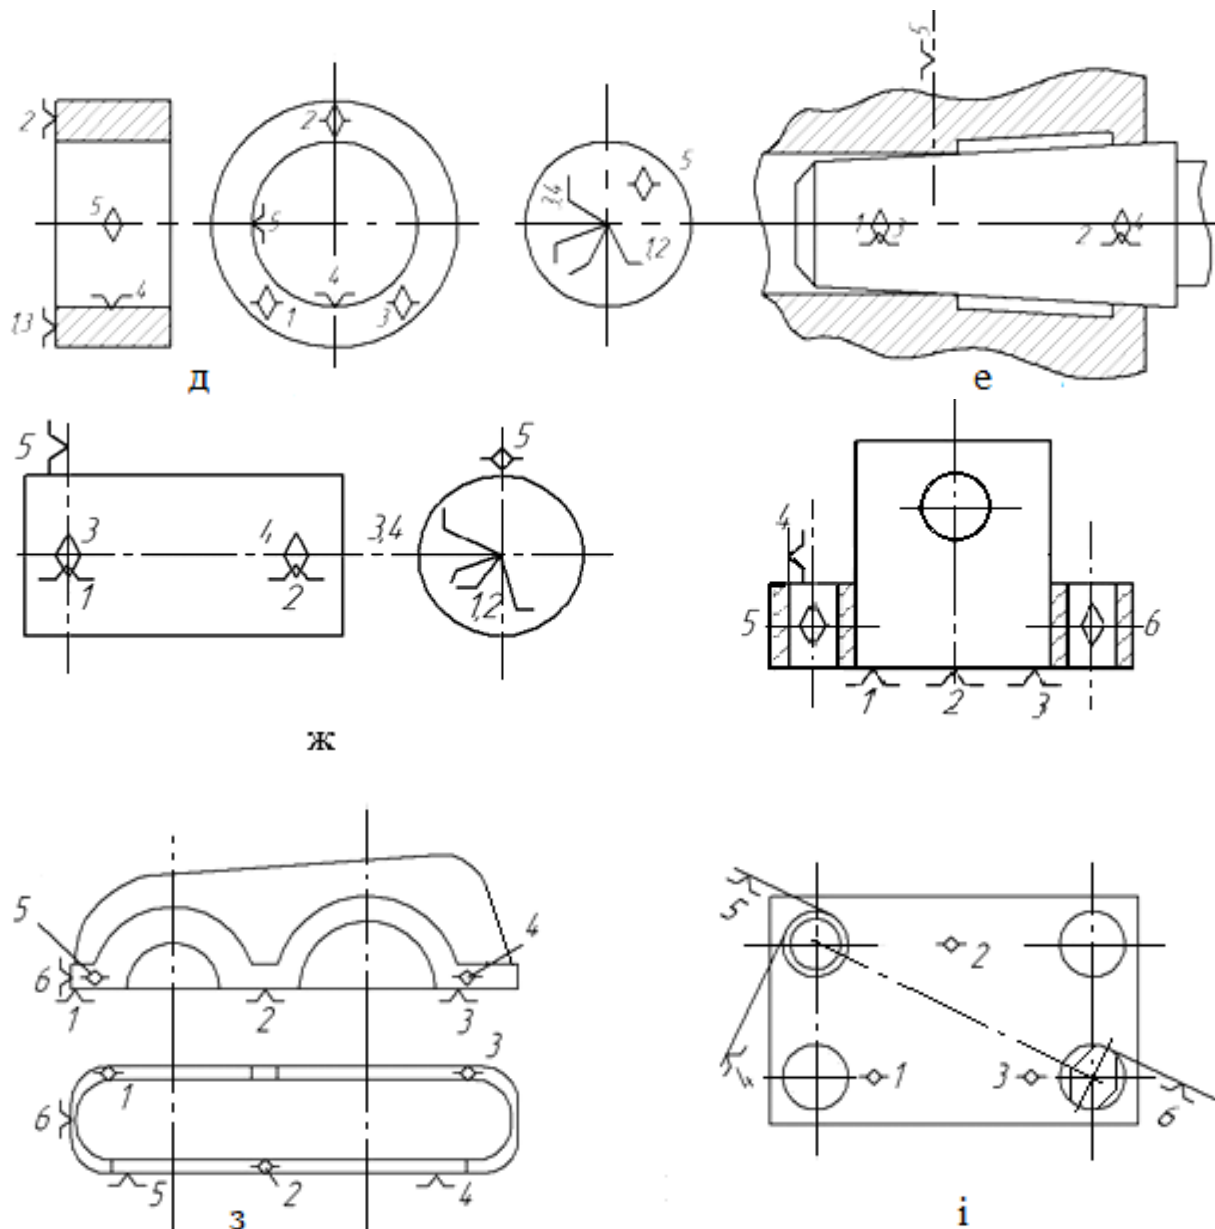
Схеми базування різних заготовок при установці короткої втулки-диска (д), за довгою конічною поверхнею (е), установці вала (ж), та корпусних деталей (з, і)
